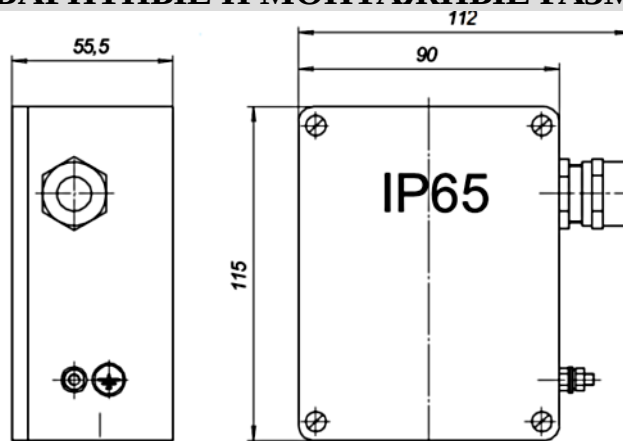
Габаритные и монтажные размеры рН-метра рН-4101 в корпусе "Д".
